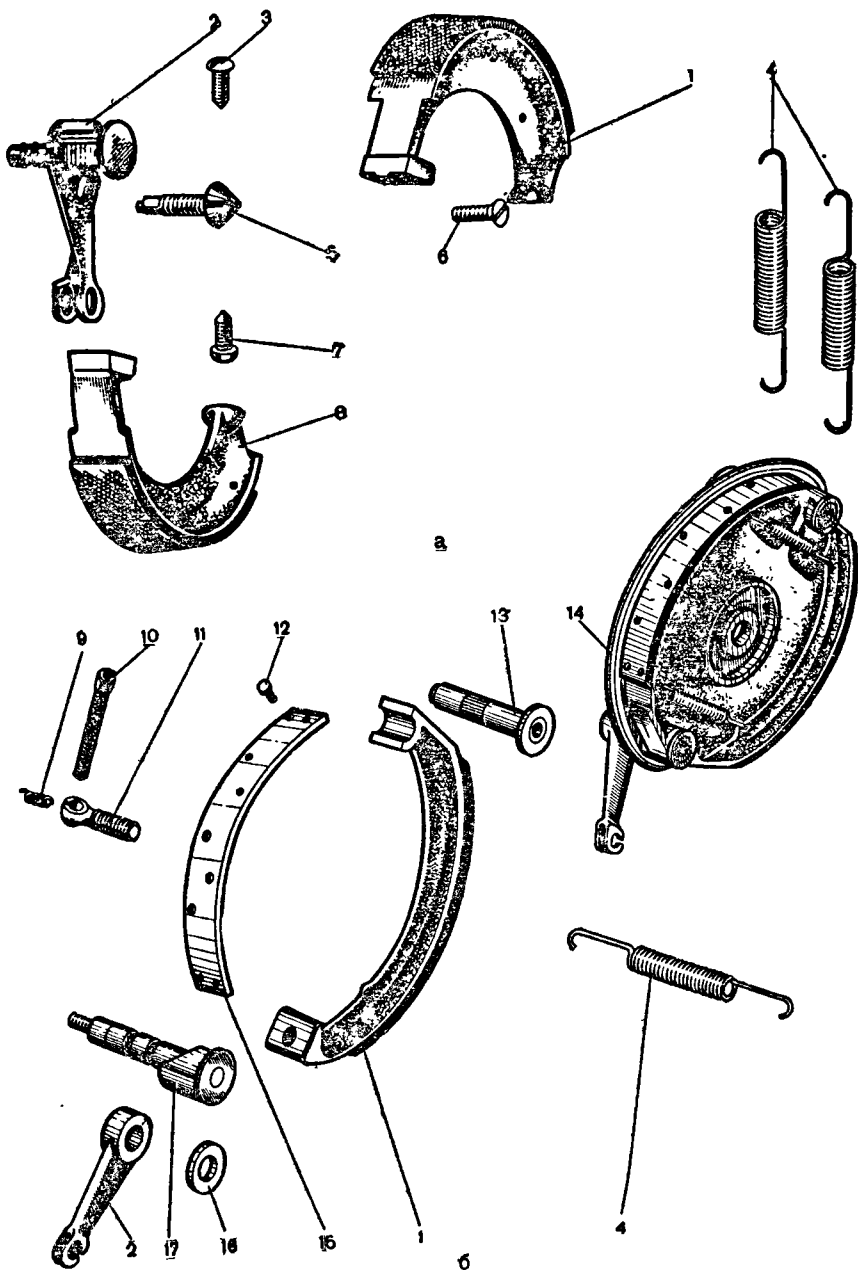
Детали тормозов мотоциклов: а — «Днепр»; б — «Урал»;
